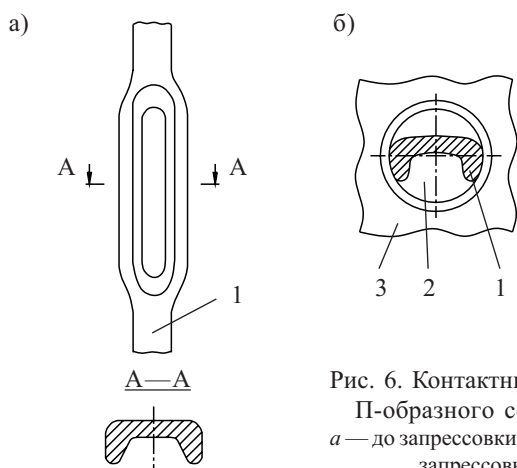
Контактный штырь П-образного сечения: а — до запрессовки; б — после запрессовки
